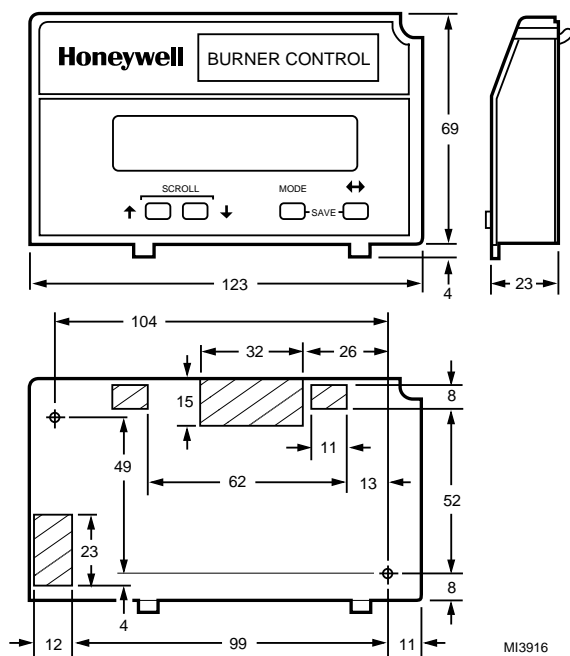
Dimensioni in millimetri per il montaggio del modulo visore con tastiera.
